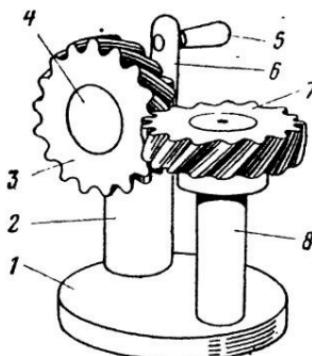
Модель передачи с винтовыми зубчатыми колесами: 1 — основание; 2 — стойка; 3 — ведущее колесо; 4 — вал привода; 5 — ручка; 6 — рычаг ручки; 7 — ведомое колесо; 8 — ось.
